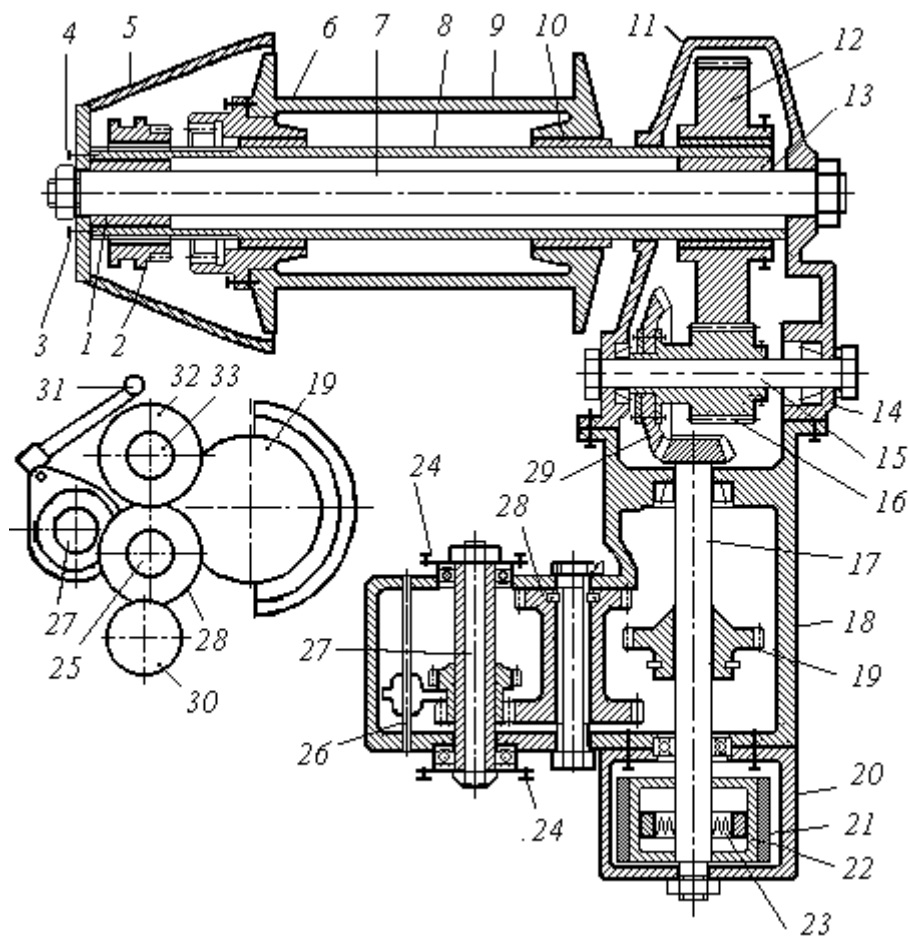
Схема устройства лебедки ТТ-4М: 1, 13 – опорные подшипники трубы; 2 – муфта включения; 3 – болт; 4 – винт установочный; 5 – опора левая; 6, 10 – подшипник барабана; 7 – ось; 8 – труба; 9 – барабан; 11 – крышка редуктора; 12 – колесо зубчатое; 14 – картер редуктора; 15 – вал; 16 – шестерня; 17 – ведущий вал-шестерня; 18 – картер раздаточной коробки; 19 – шестерня реверсивная; 20 – кожух тормоза; 21 – лента тормозная; 22 – шкив; 23 – муфта свободного хода; 24 – вилки карданных валов; 25, 33 – оси; 26 – подвижный блок шестерен; 27 – ведущий вал раздаточной коробки; 28 – блок промежуточных шестерен; 29 – ведомое коническое колесо; 30 – шестерня вала отбора мощности; 31 – рукоятка включения привода; 32 – блок шестерен заднего хода
